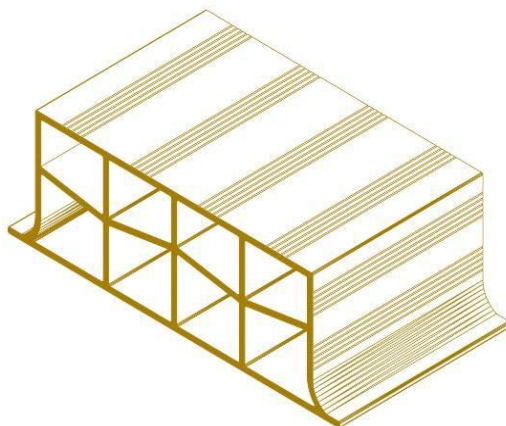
Vista tridimensionale di un tipico elemento di alleggerimento
